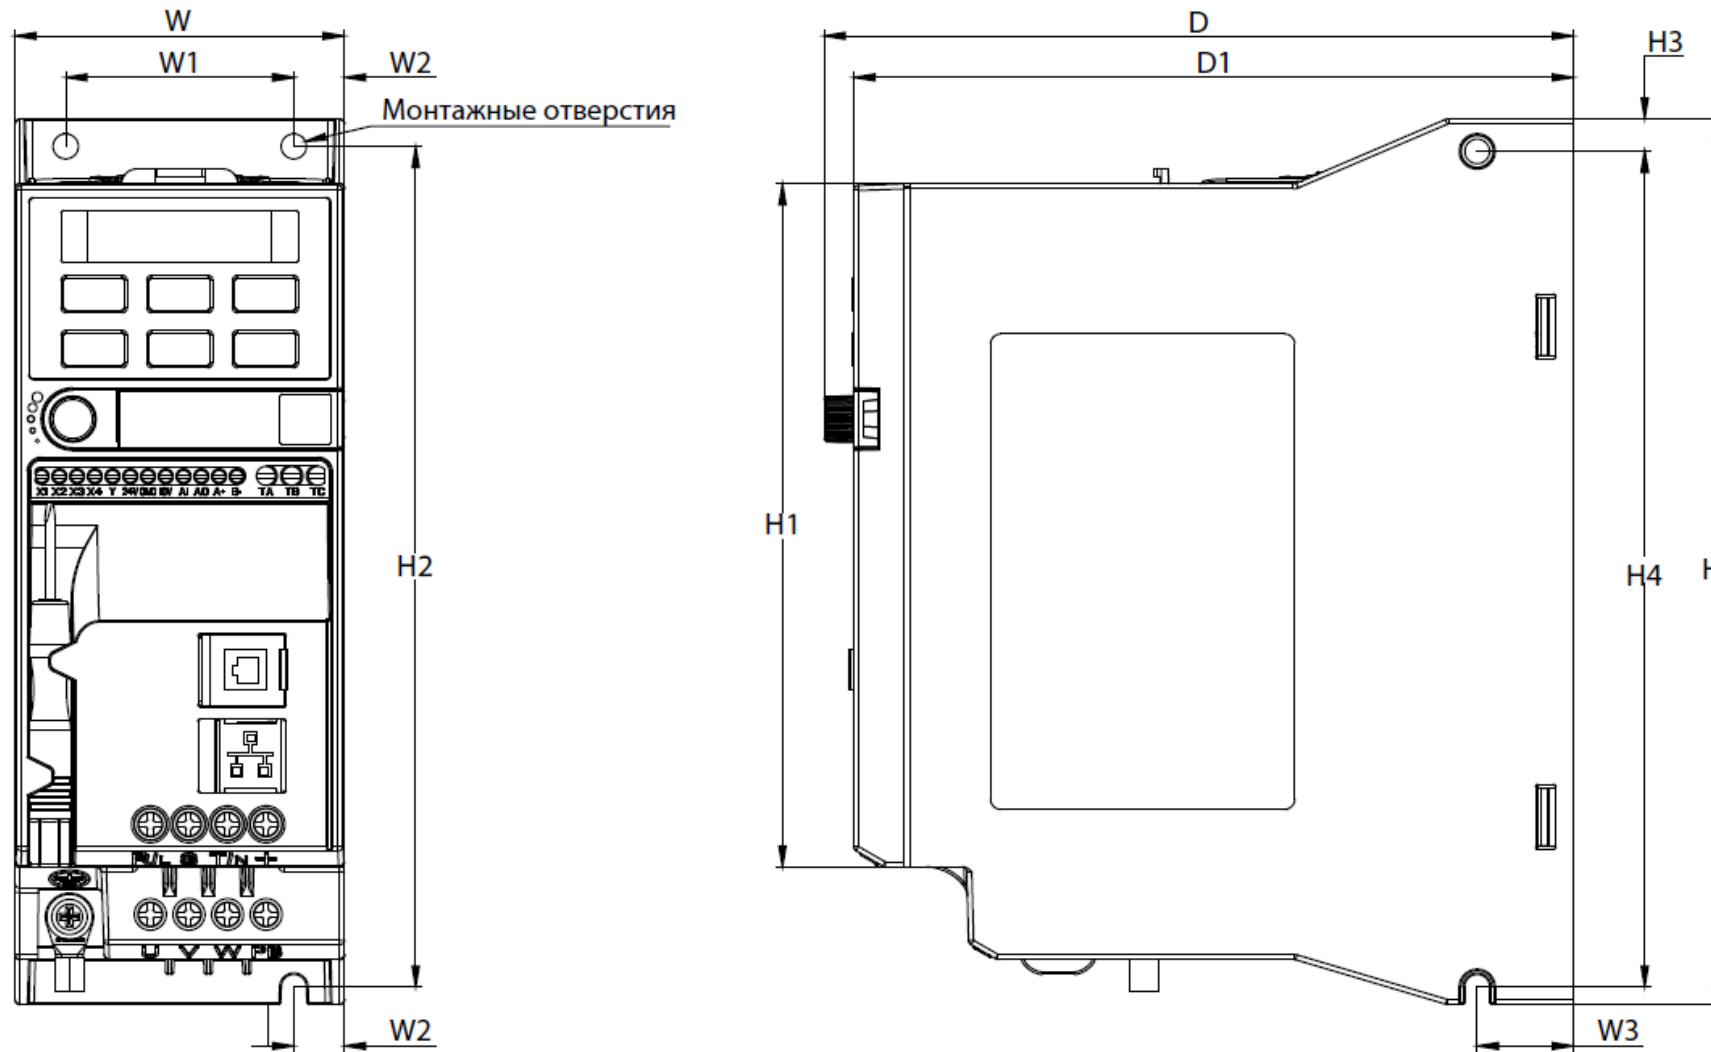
Чертеж преобразователя частоты типоразмер А1
